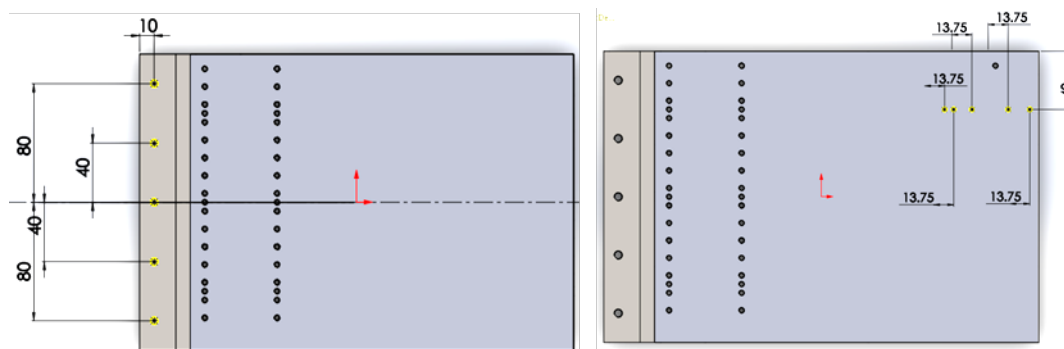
Posicionamiento de barrenos a) sujetador, b) tope móvil.
